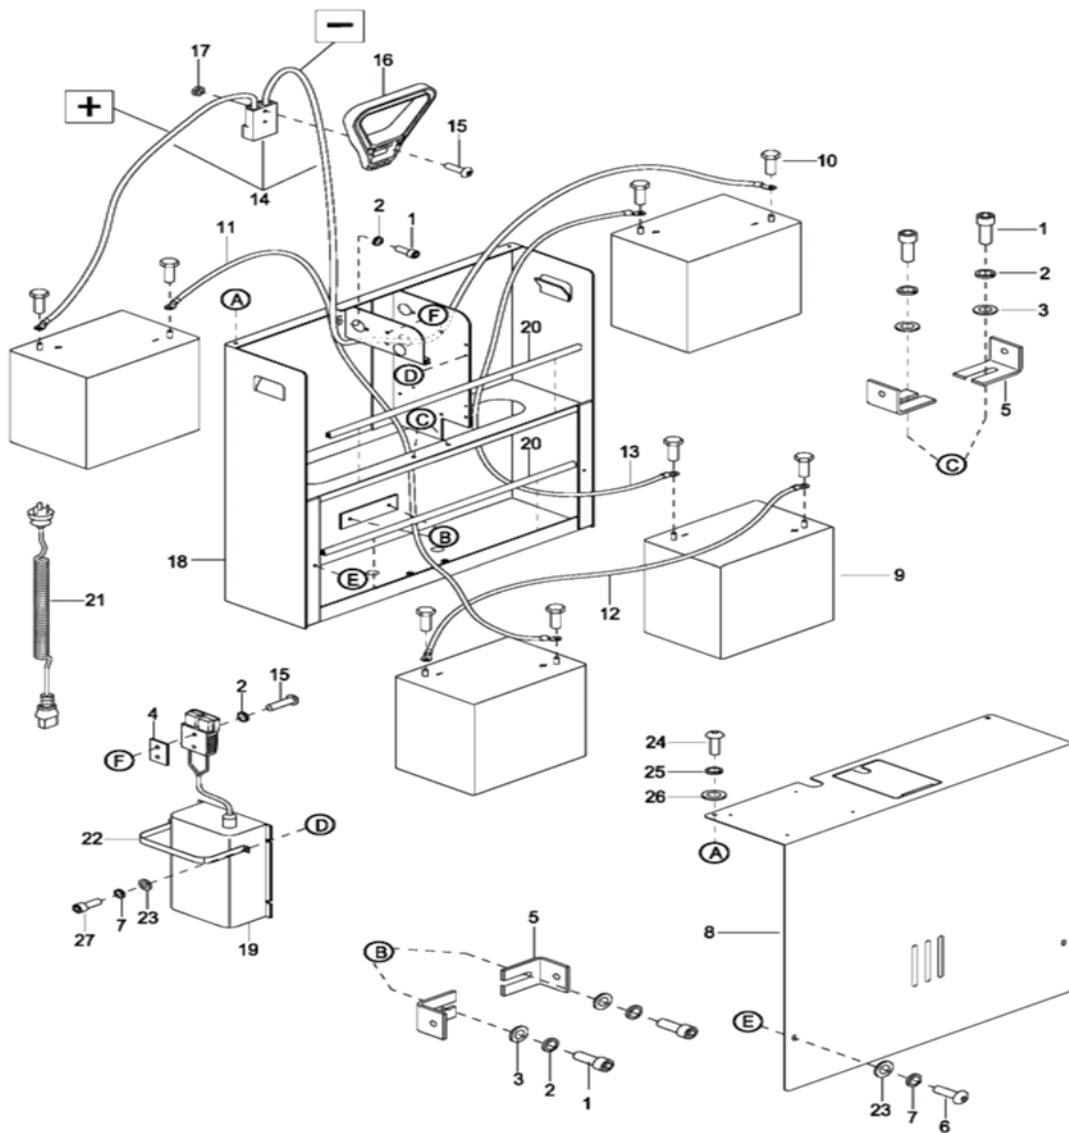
ASSEMBLAGE DE BATTERIE - CONFIGURATION D'USINE
